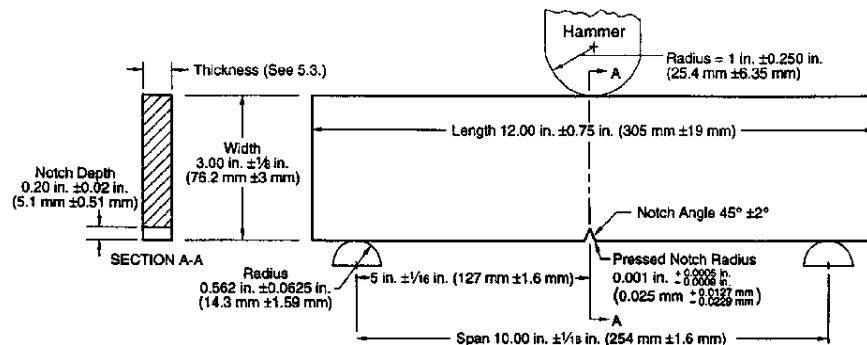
Corpo-de-prova de ensaio DWT. (API 1996)
